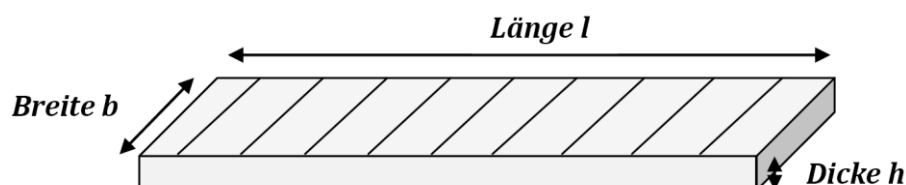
Skizze einer Biegeprobe mit Definition der Bemaßungen
